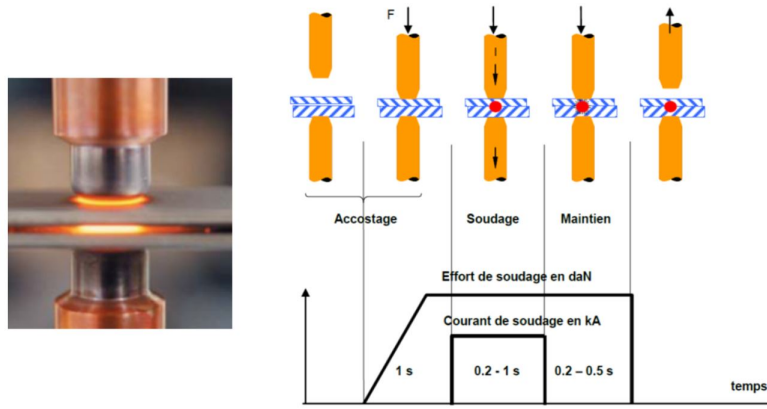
Principe du soudage de points par résistance [1]
